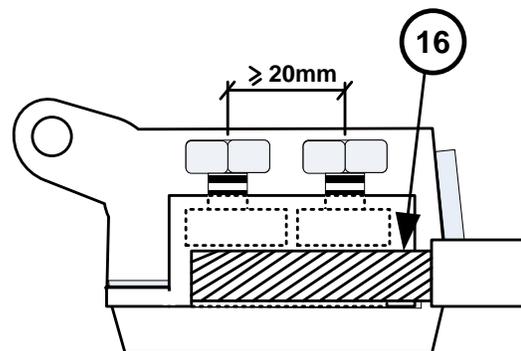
c. Diseño de la bornera con doble tornillo, una vez montado.
